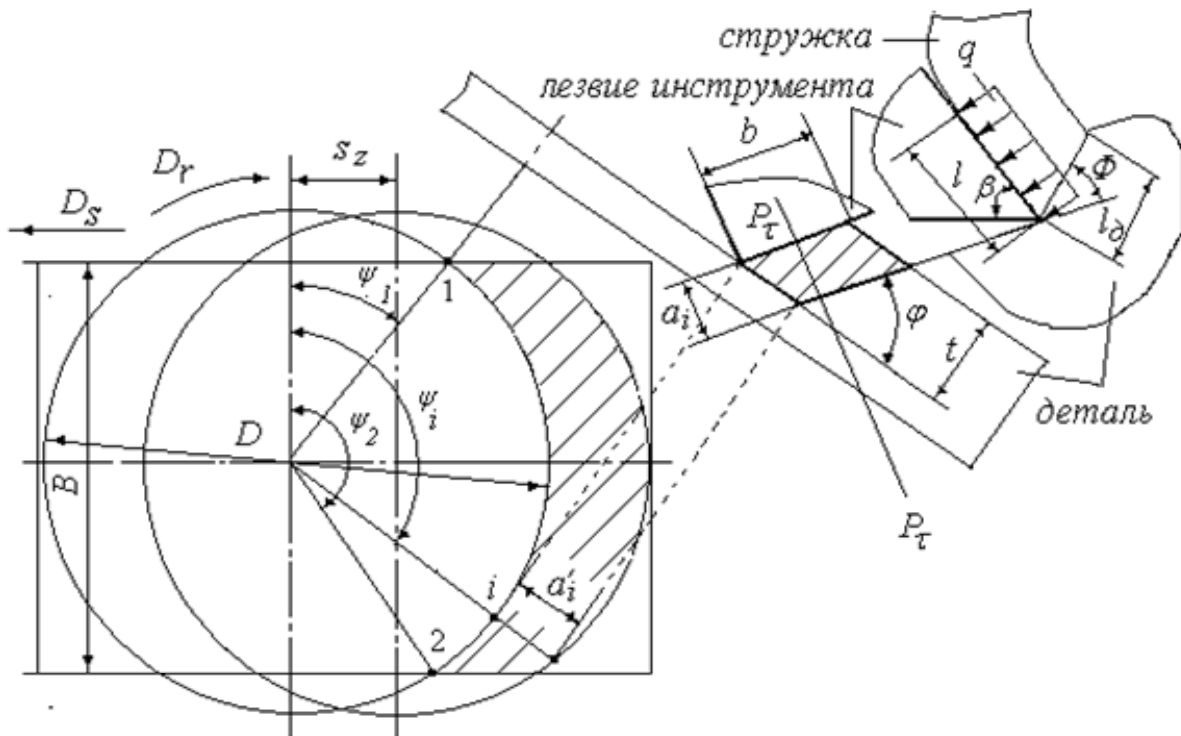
Схема для определения основных параметров процесса фрезерования торцовыми фрезами
